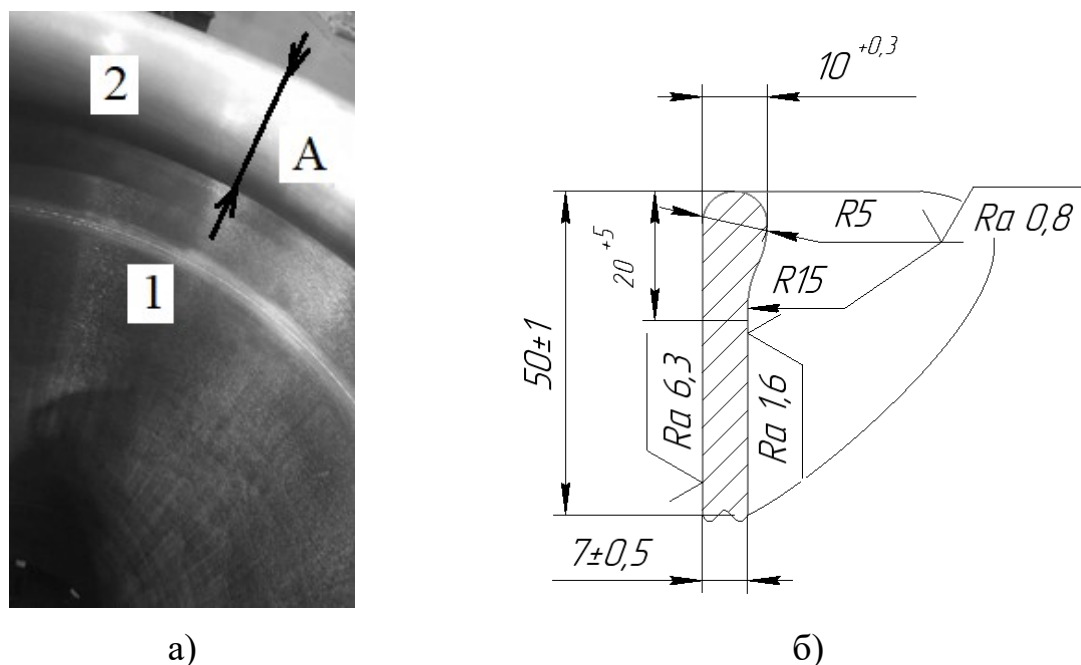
Внутренняя поверхность корпуса ЭТ, где:
